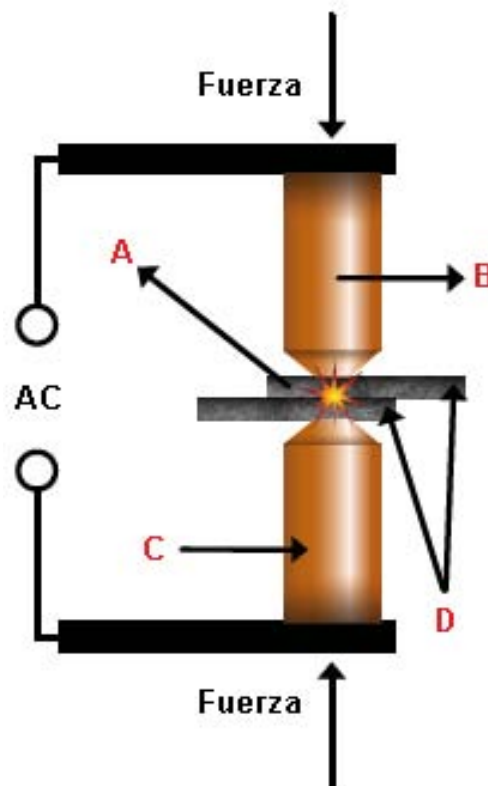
Puntos clave de la soldadura por puntos.
